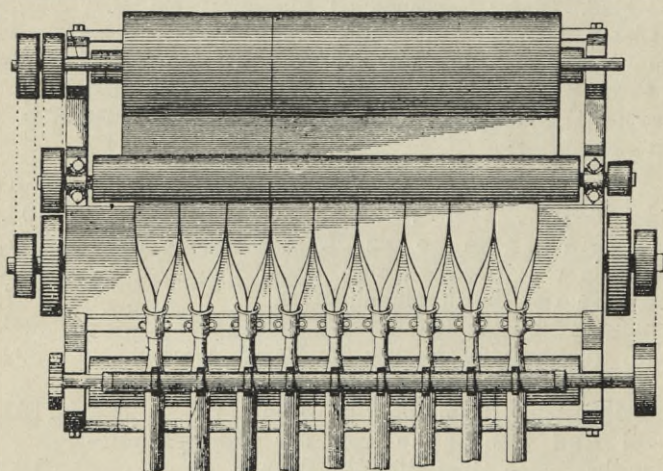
Doughtys Schneidemaschine für Luftschläuche.
